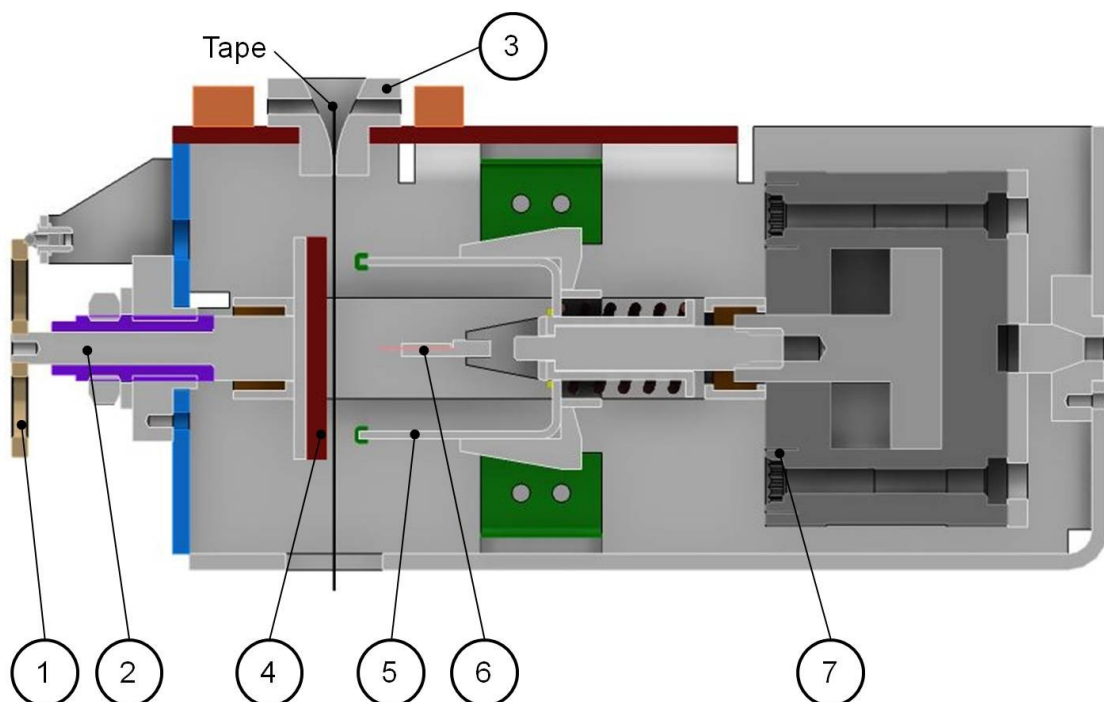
Schnittansicht vom Schneidemechanismus (1. Handrad mit federndem Druckstück, 2. Gewindebolzen, 3. Führungsblöcke, 4. Prallblende, 5. gefederter und geführter Niederhalter, 6. Klinge und -aufnahme, 7. Kompaktzylinder).
